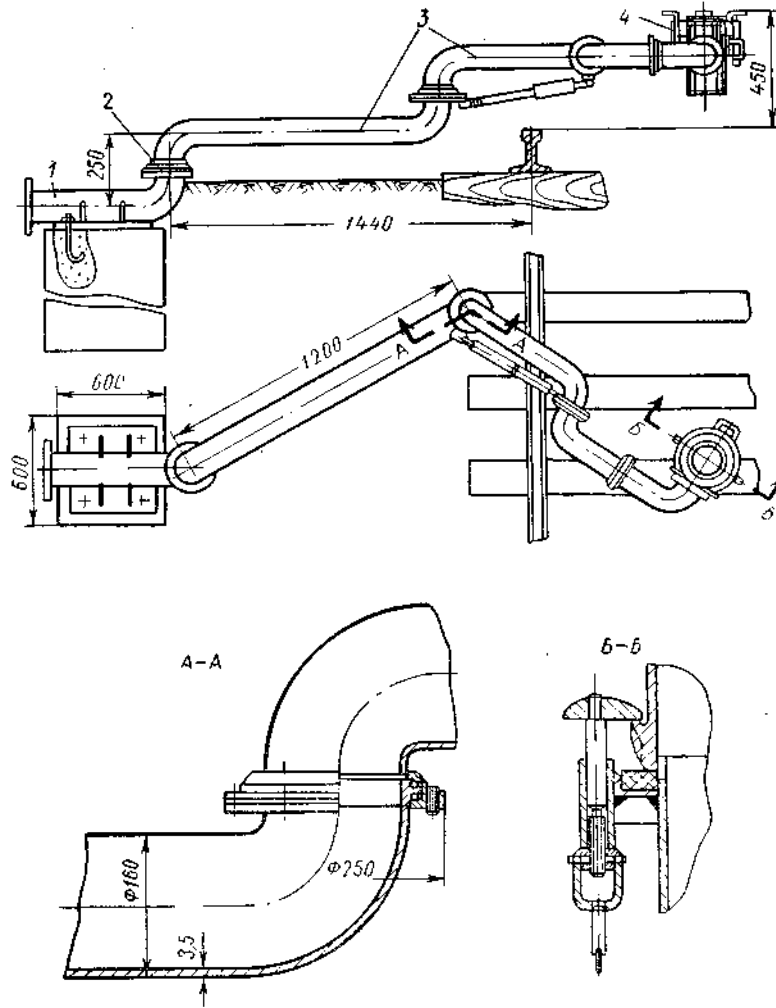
Устройство для нижнего слива нефтепродуктов из железнодорожной цистерны (СЛ-9): 1 – неподвижный патрубок для присоединения к сливному коллектору; 2 – отвод; 3 – шарнирно сочлененный трубопровод; 4 – соединительная головка
